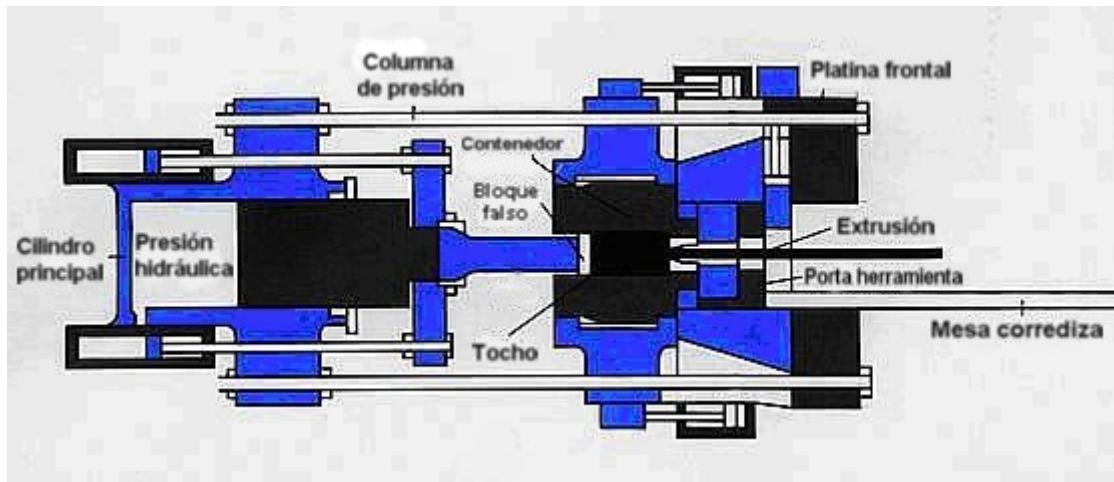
Representación esquemática de una prensa de extrusión horizontal. La extrusión es de izquierda a derecha.[14]
